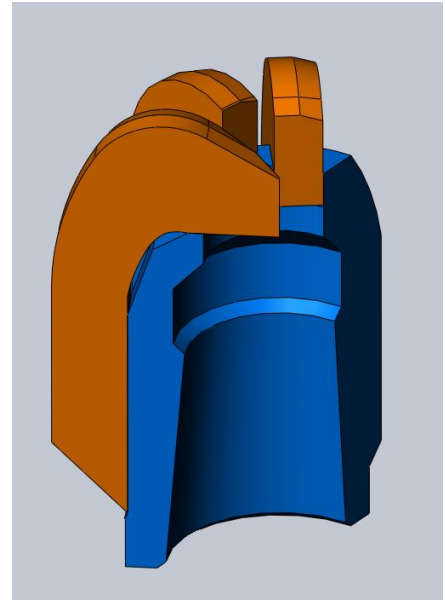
3Д-модель корпусу долота із встановленими лопатями в пази
